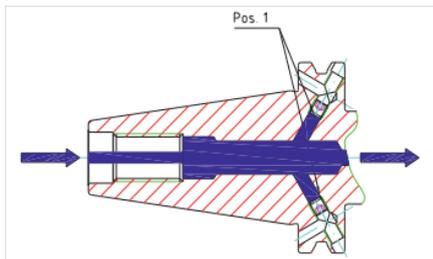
Kühlmittelzuführung *Form AD/JD
